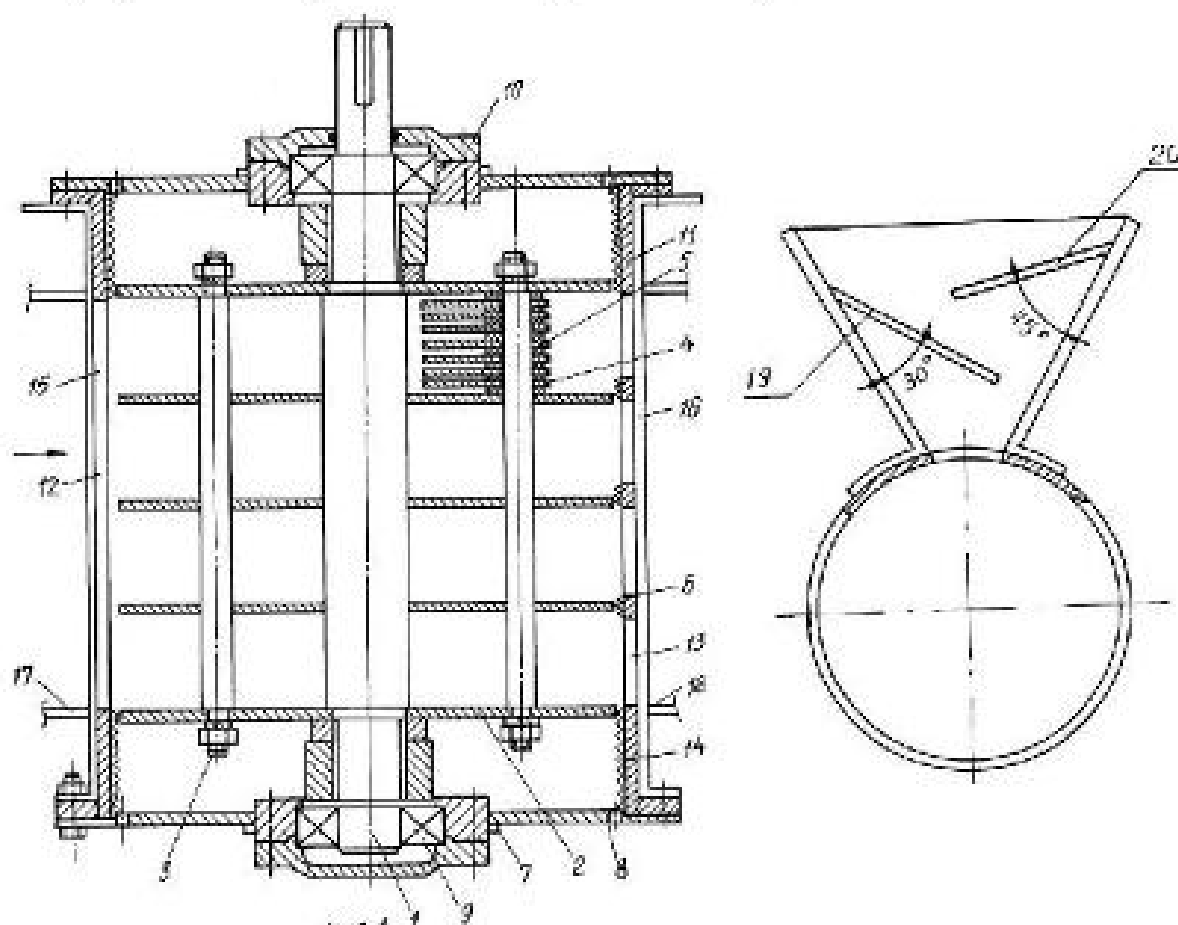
Молотковая дробилка Патент РФ 2106911
